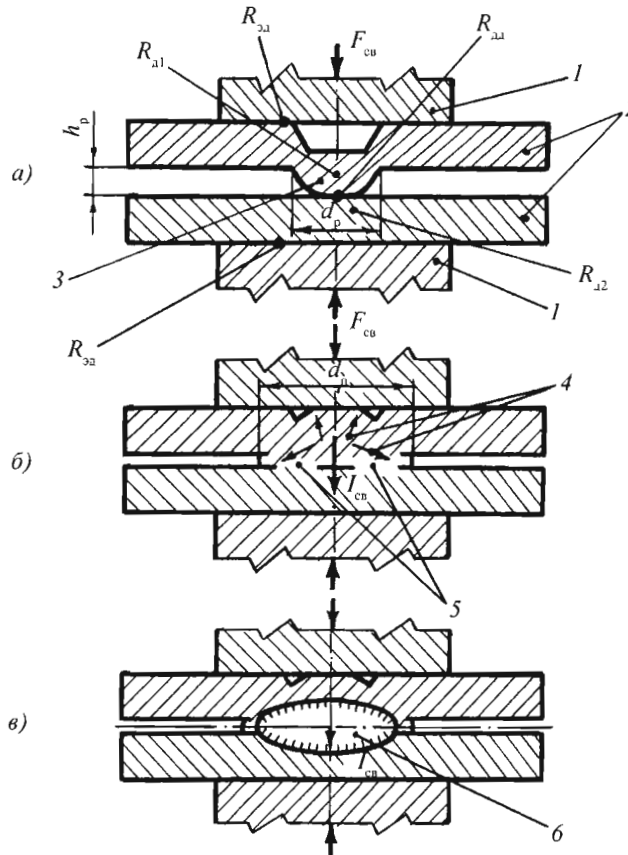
Схема процесса рельефной сварки:
